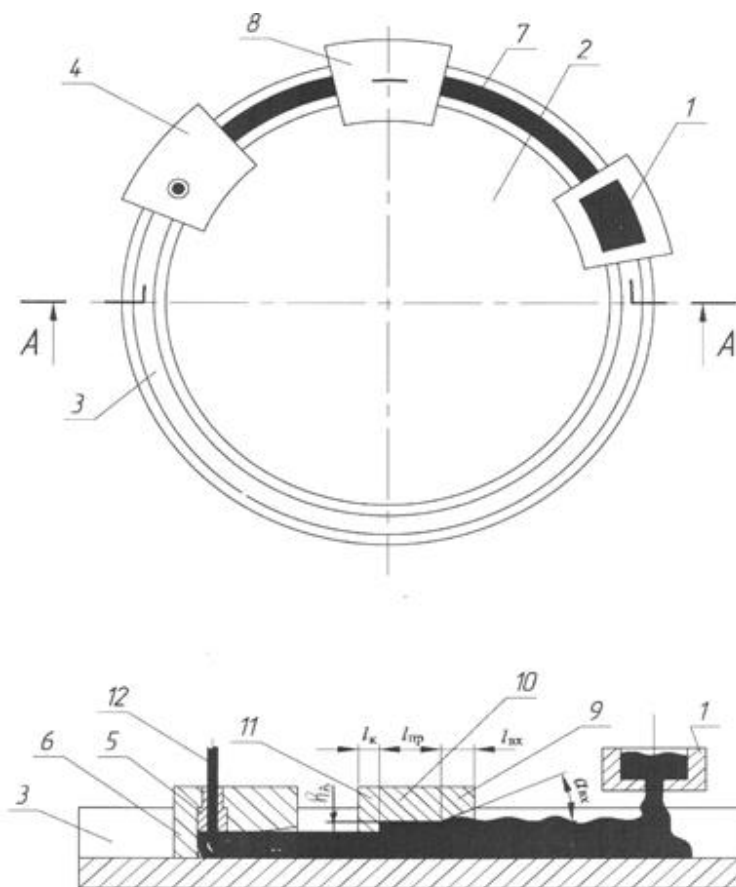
Схема установки непрерывного литья и прессования методом Конформ
